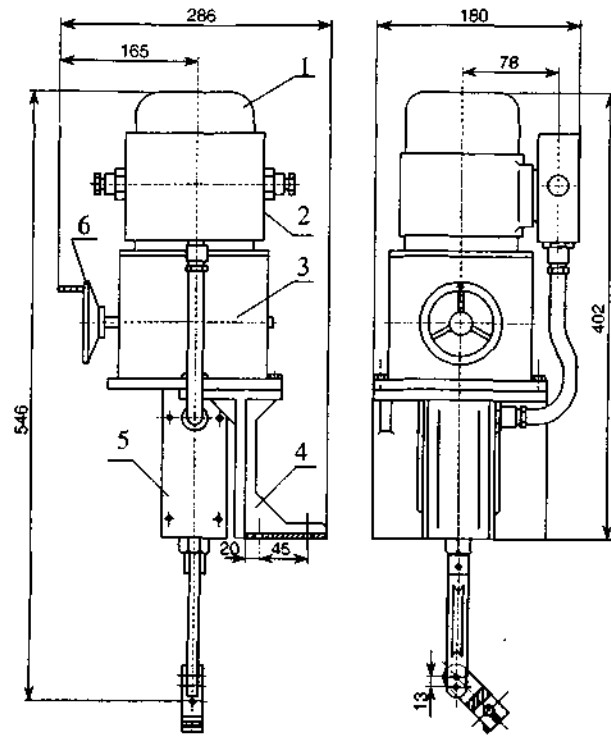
Габаритні розміри механізму типу ЕСПА: 1- електродвигун; 2 – розподільча коробка; 3 – редуктор; 4 – стійка; 5 – керуюча коробка; 6 – ручний дублер.
